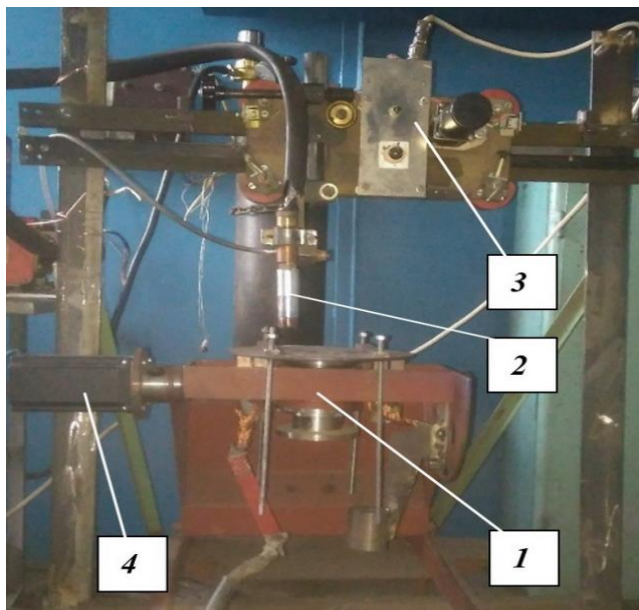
Зовнішній вигляд станини та основні її вузли: 1 – рухомий стіл, 2 – зварювальний пальник, 3 – рухома каретка, 4 – кроковий двигун
